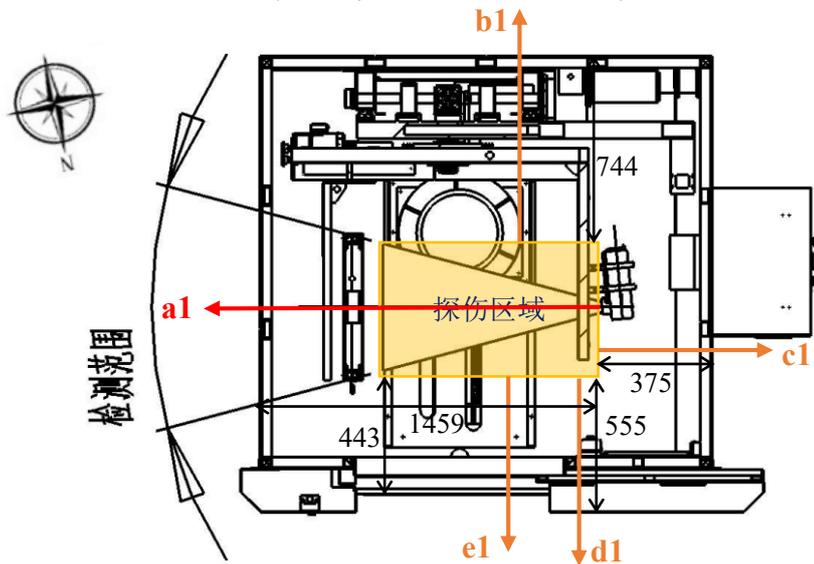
辐射屏蔽计算预测点位平面图（沿塘河路厂区）（单位：mm）
